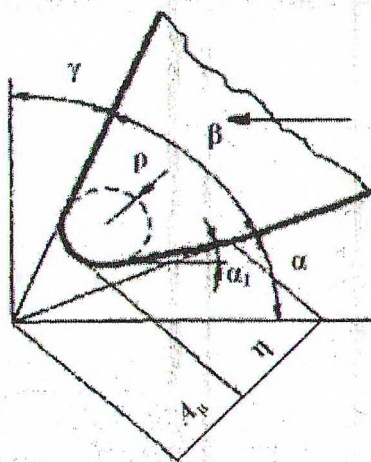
Характер износа резца при обработке ДСП твердосплавным фрезерным инструментом
